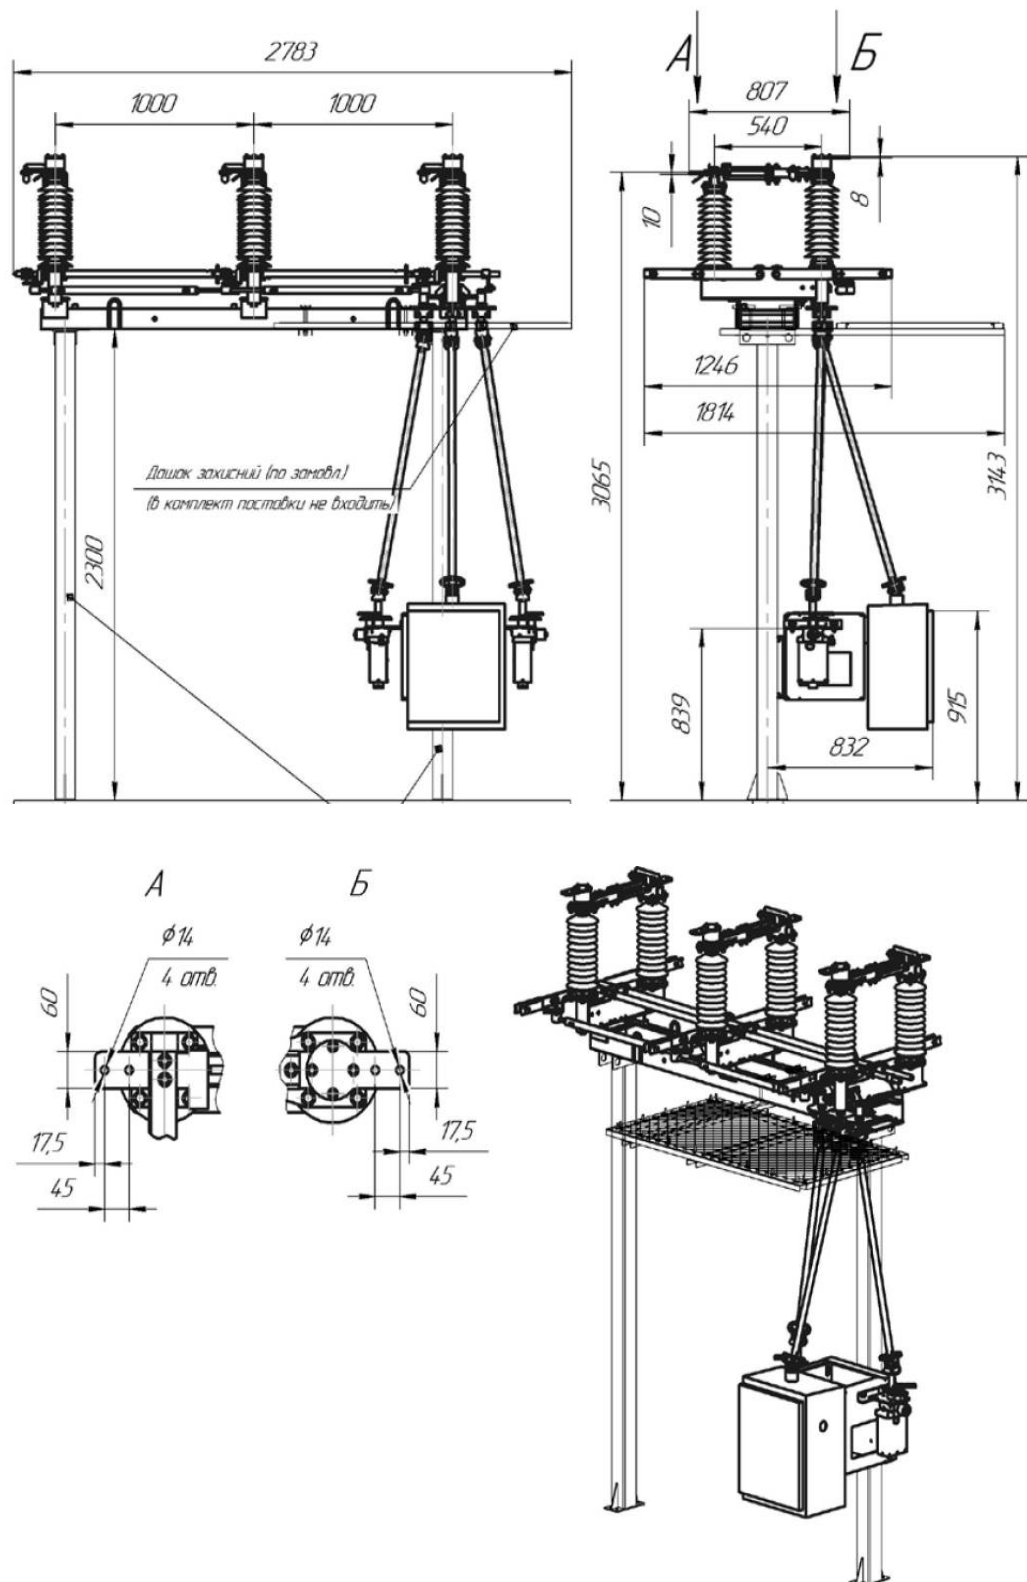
габаритные, установочные и присоединительные размеры базового исполнения трехфазного разъединителя РГП-НТ.2-35 / 1000 У1 с электродвигательным приводом главных ножей и ручными приводами ПРН-35 У1 заземляющих ножей
